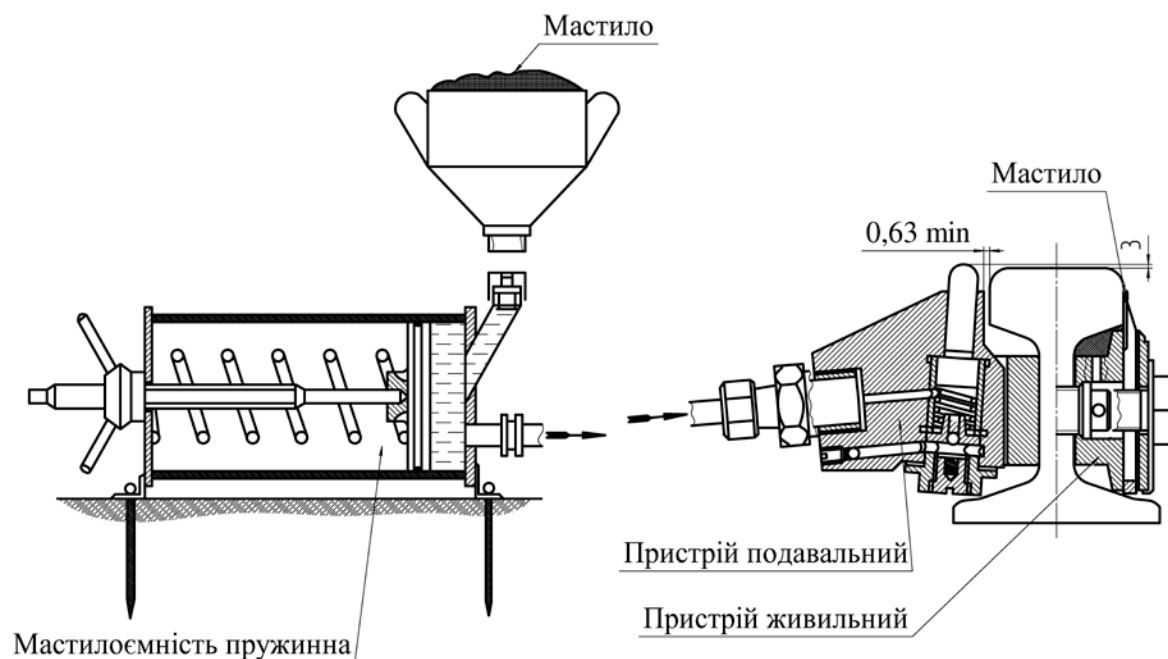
Загальний вид колійного рейкозмащувача проекту 1901.00.000.СБ
